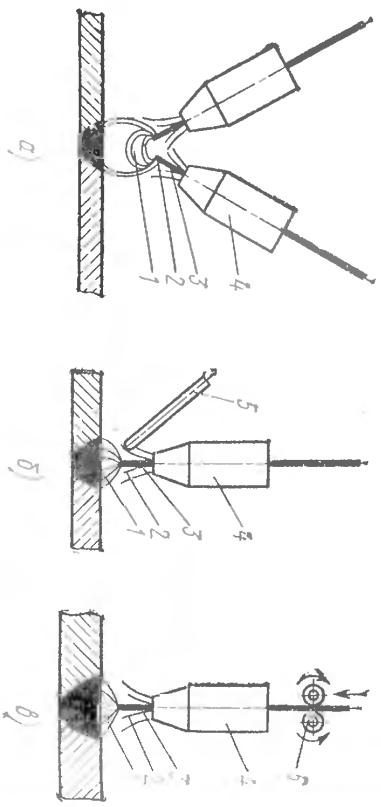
Способы дуговой сварки в защитном газе:
